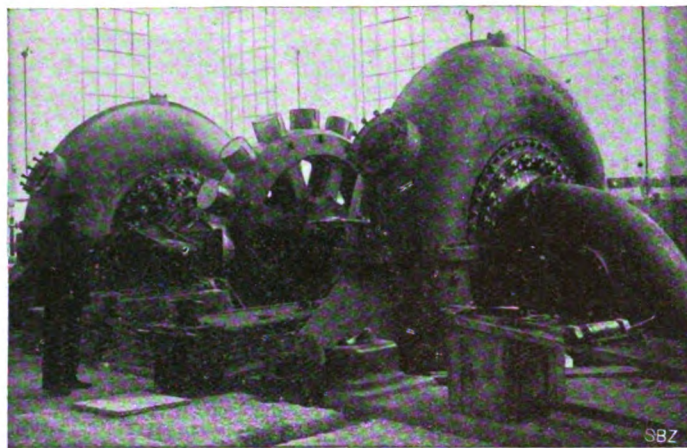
Maschinengruppe von 18000 PS, in Montage.
